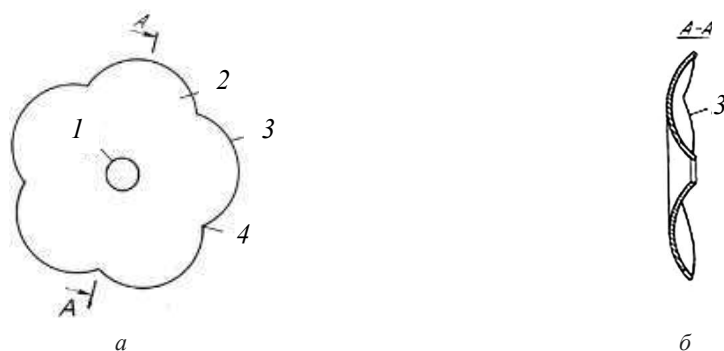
Схема диска для пахоты: а – вид спереди; б – разрез А-А;
